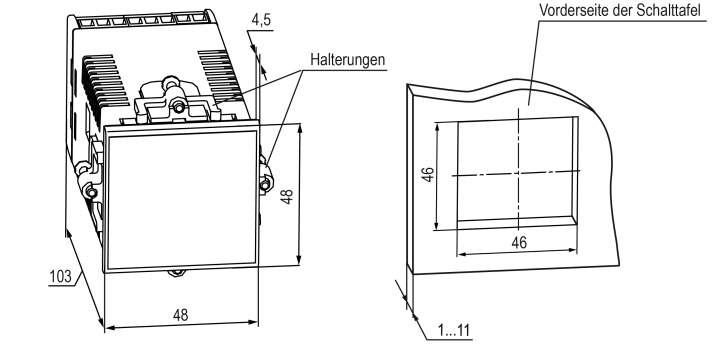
Abmessungen des P5-Gehäuses und des Montageausschnitts
